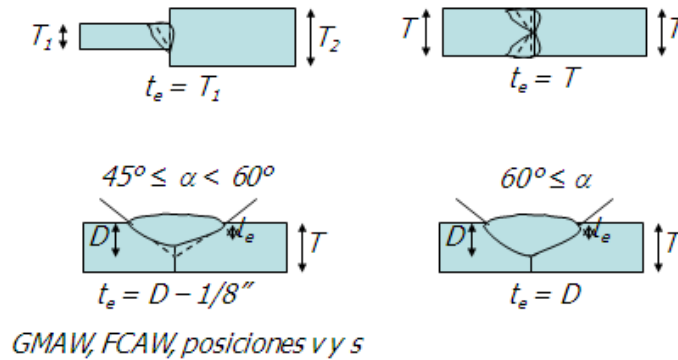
Peralte efectivo de la garganta para soldadura de penetración parcial.
